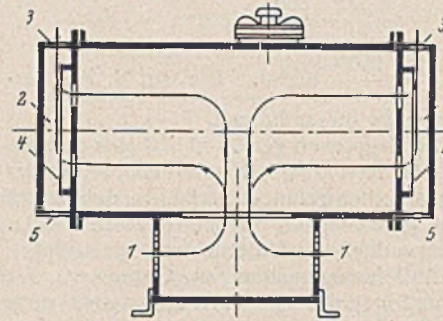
Einzelschweißumformer der Siemens-Schuckertwerke AG. in Eingehäuseausführung mit einem Regelbereich von 50 bis 250 A bei 15 bis 25 V.
